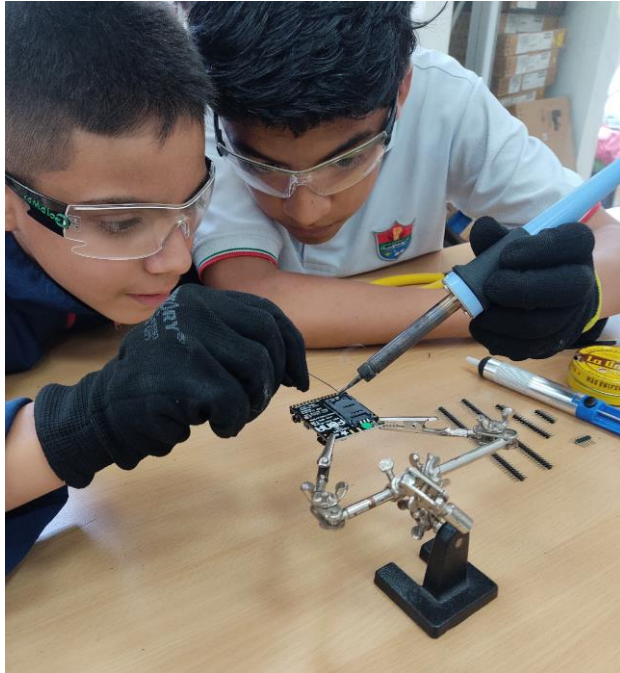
Proceso de soldadura en el módulo FONA800 para instalación en robot. Fuente: Autor.
